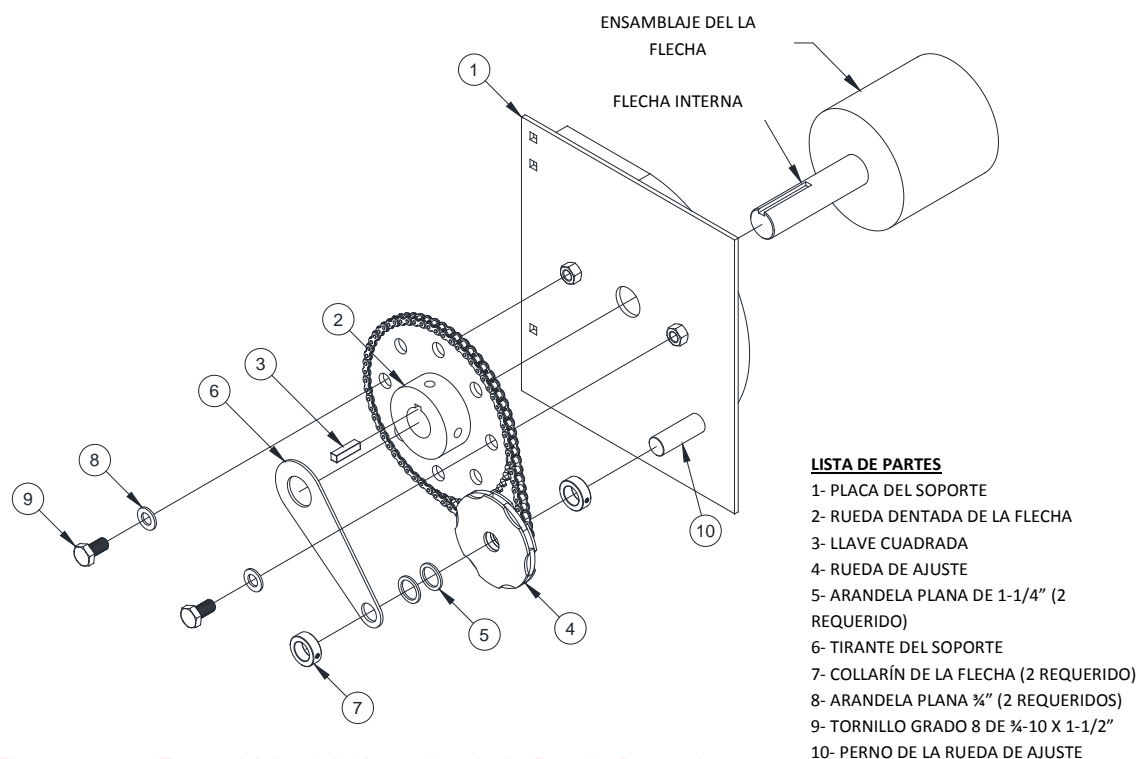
Ensamblaje del Ajustador de la Rueda Dentad
